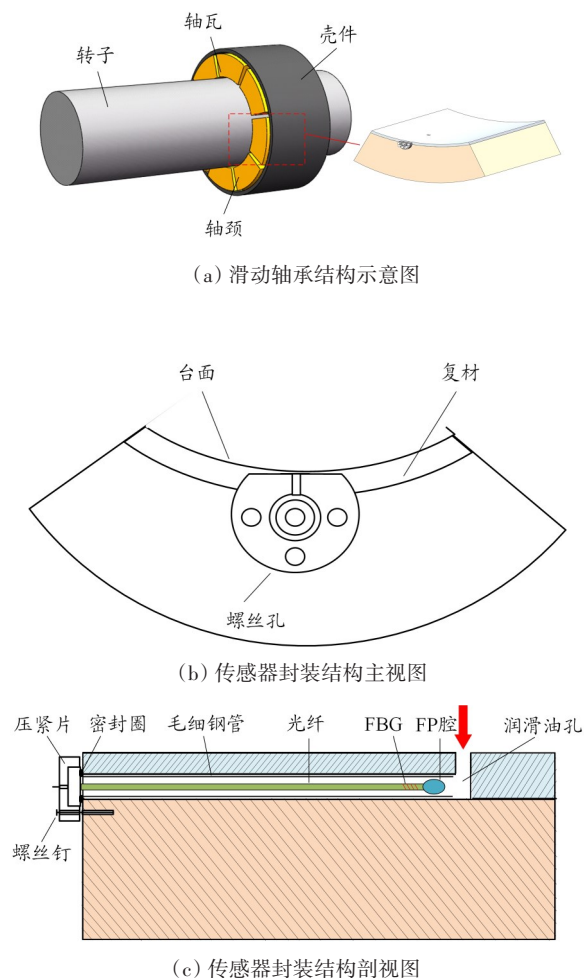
传感器滑动轴承结构示意图、传感器封装结构主视图及剖视图
